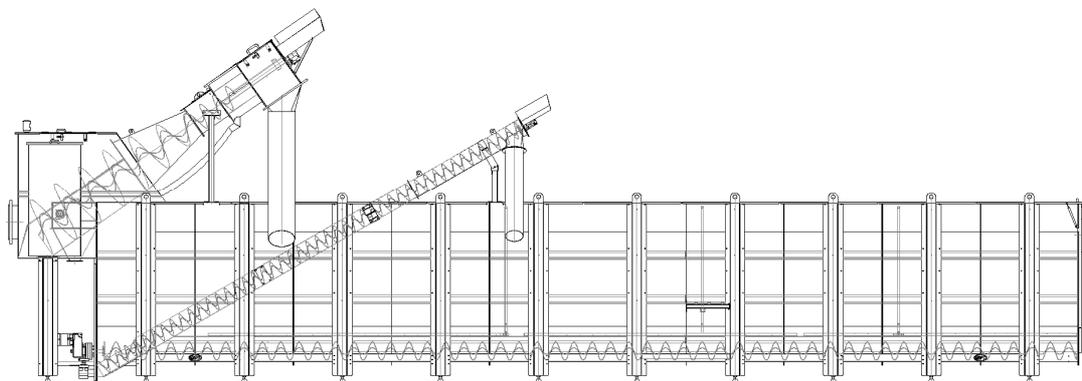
Sezione tipo nuovo impianto compatto in sostituzione di quello previsto in progetto.
